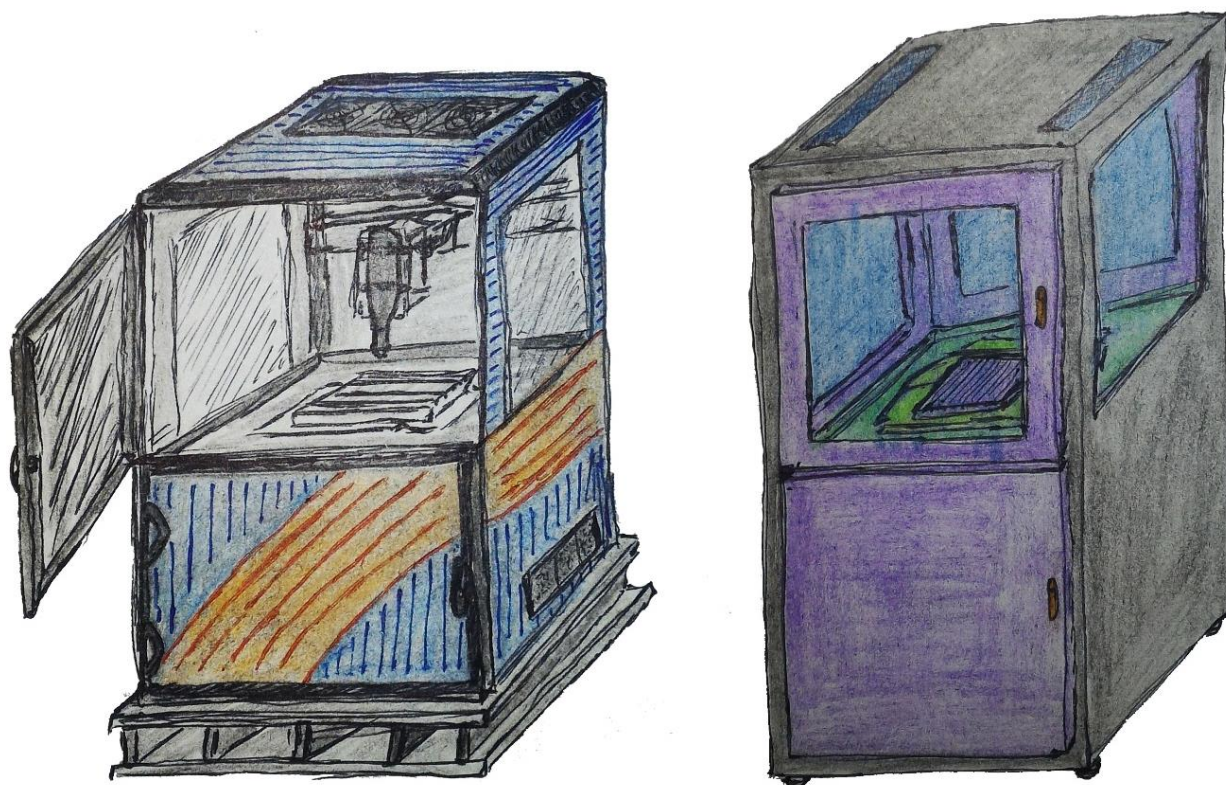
Концепт автоматизированной установки для исследований процессов дуговой сварки и наплавки
